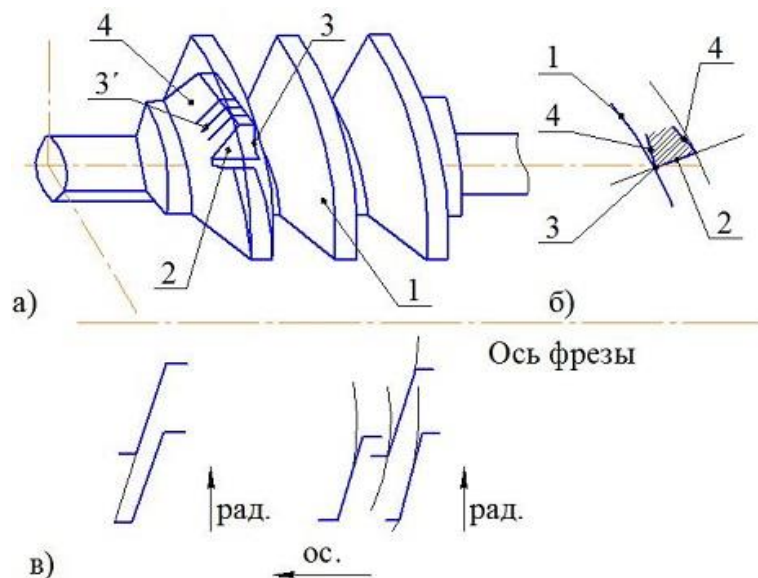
Определение профиля зубьев червячной фрезы (а);
